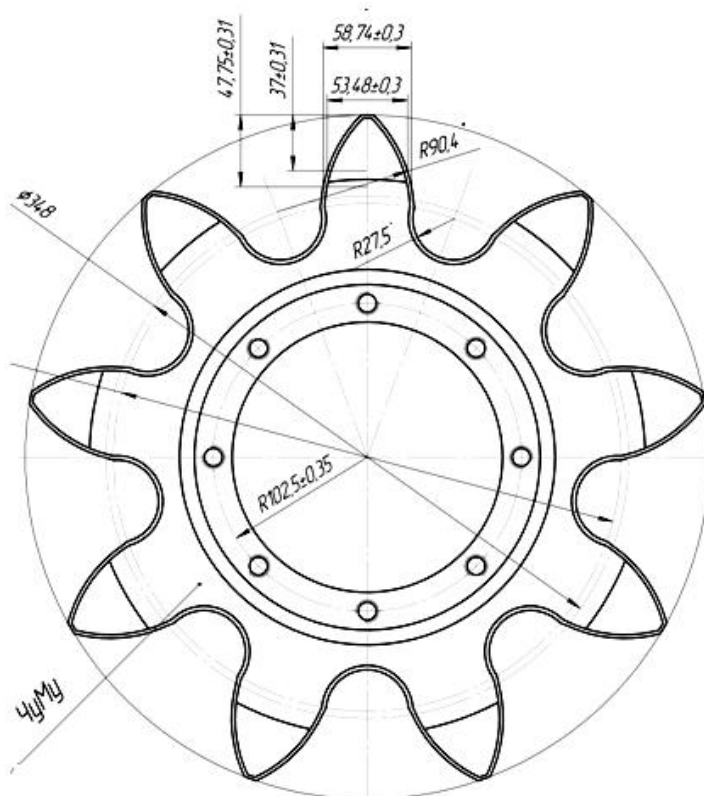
Вид зубчатого колеса БСП очистного комбайна РКУ13
